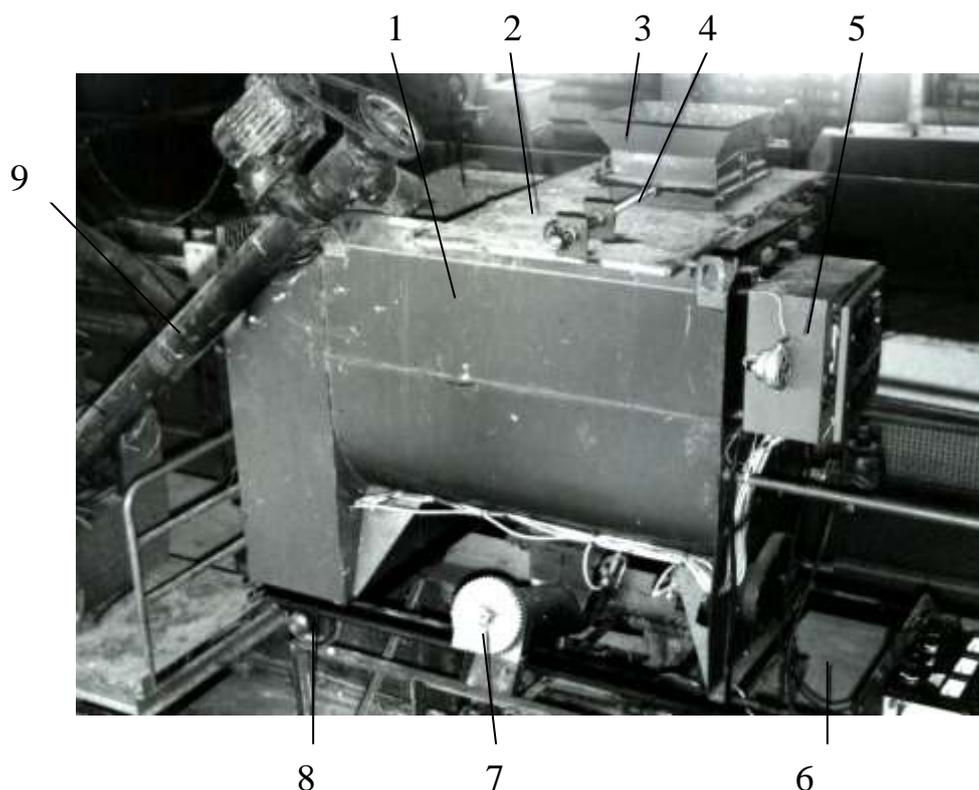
Общий вид агрегата (вид сбоку)
